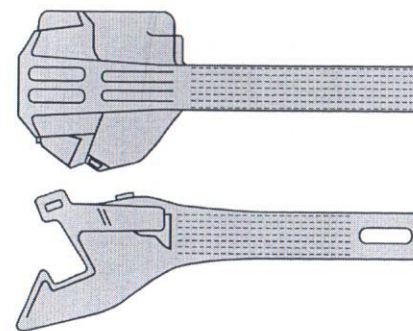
Контроль хвостовика корпуса автосцепки
